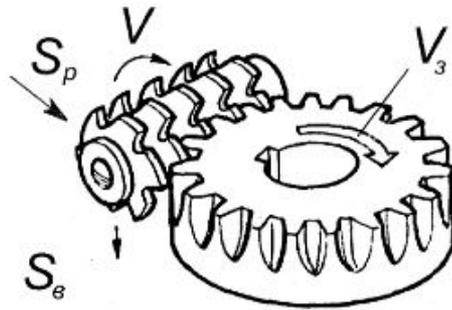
Нарезание зубьев цилиндрического колеса червячной фрезой
